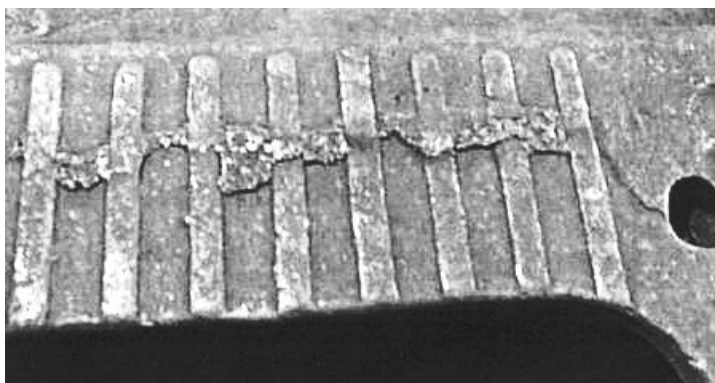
Отливка «Балансир» с дефектом «Ужимина»
